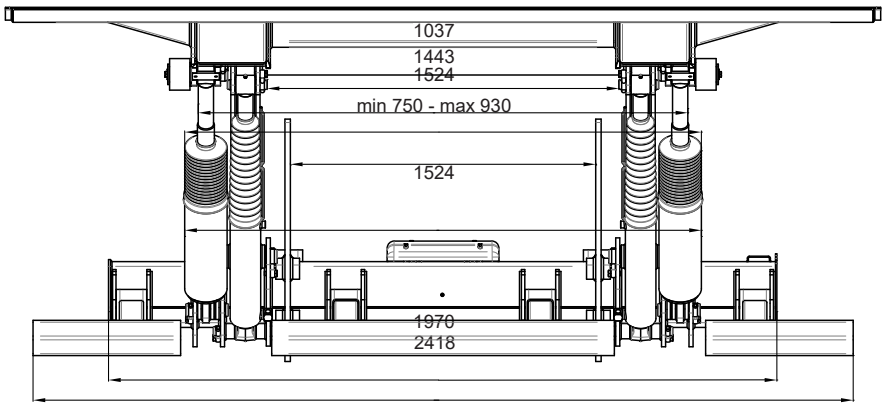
Dimensiones de instalación. ZHD 3000-150
